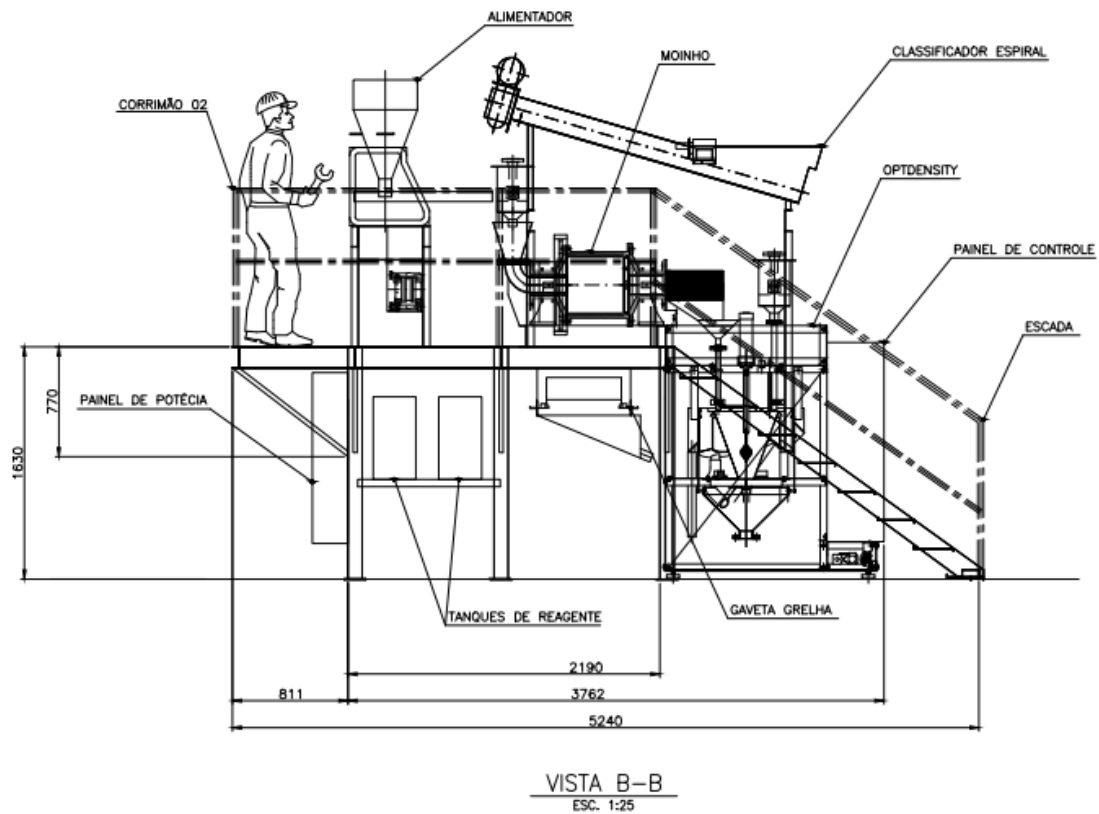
Vista B-B do Desenho da Planta Piloto.
